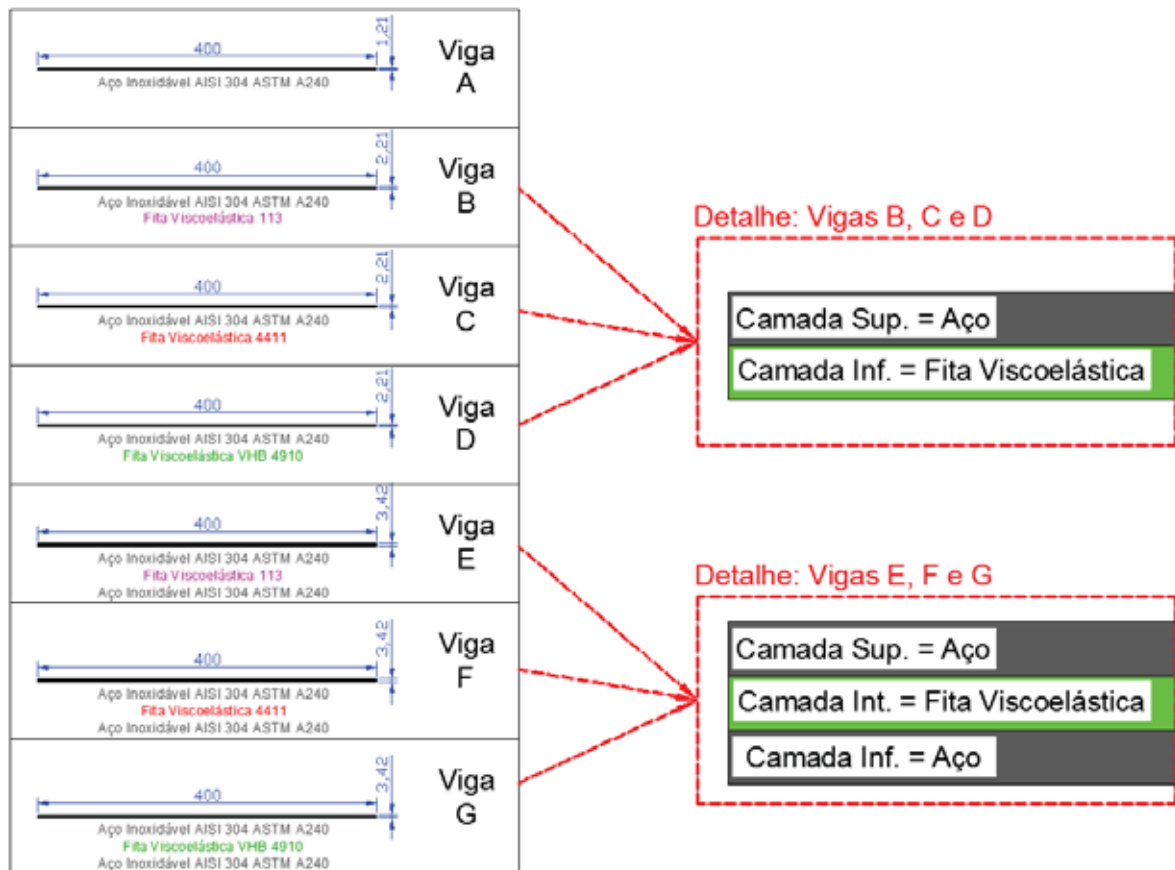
Arranjos experimentais utilizados de vigas: vigas de 24x400mm.
